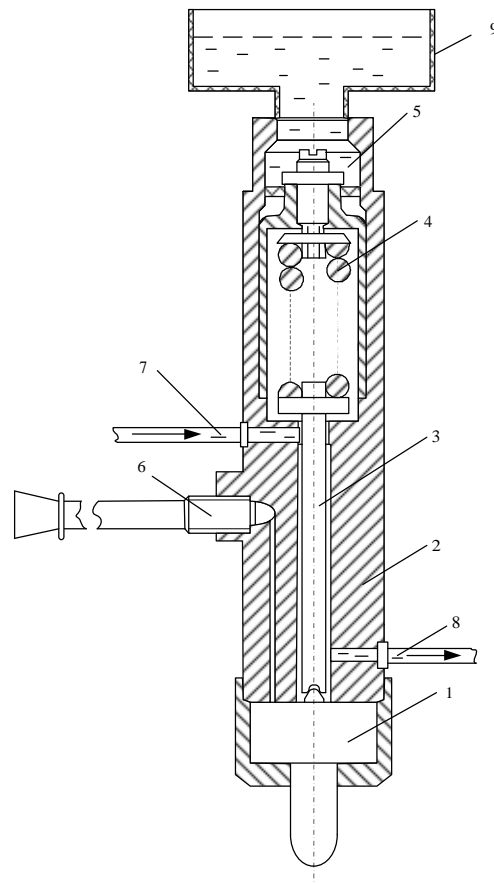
Схема экспериментального образца форсунки: 1- распылитель; 2- корпус; 3-штанга; 4- пружина; 5- полость охладителя; 6- трубопровод; 7,8- штуцера с охлаждающим топливом; 9- ёмкость для охлаждающего топлива
